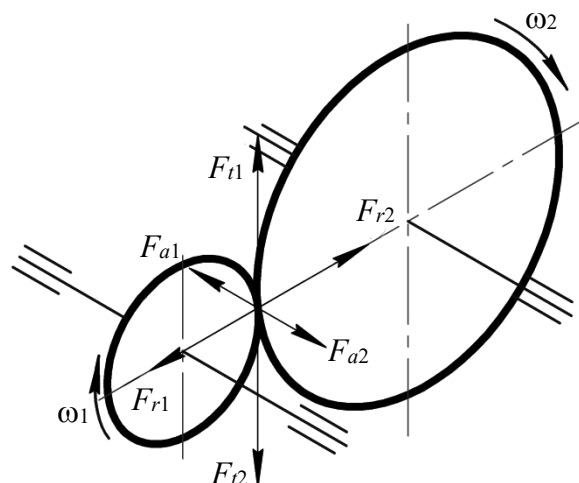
Схема сил в цилиндрической косозубой зубчатой передаче
